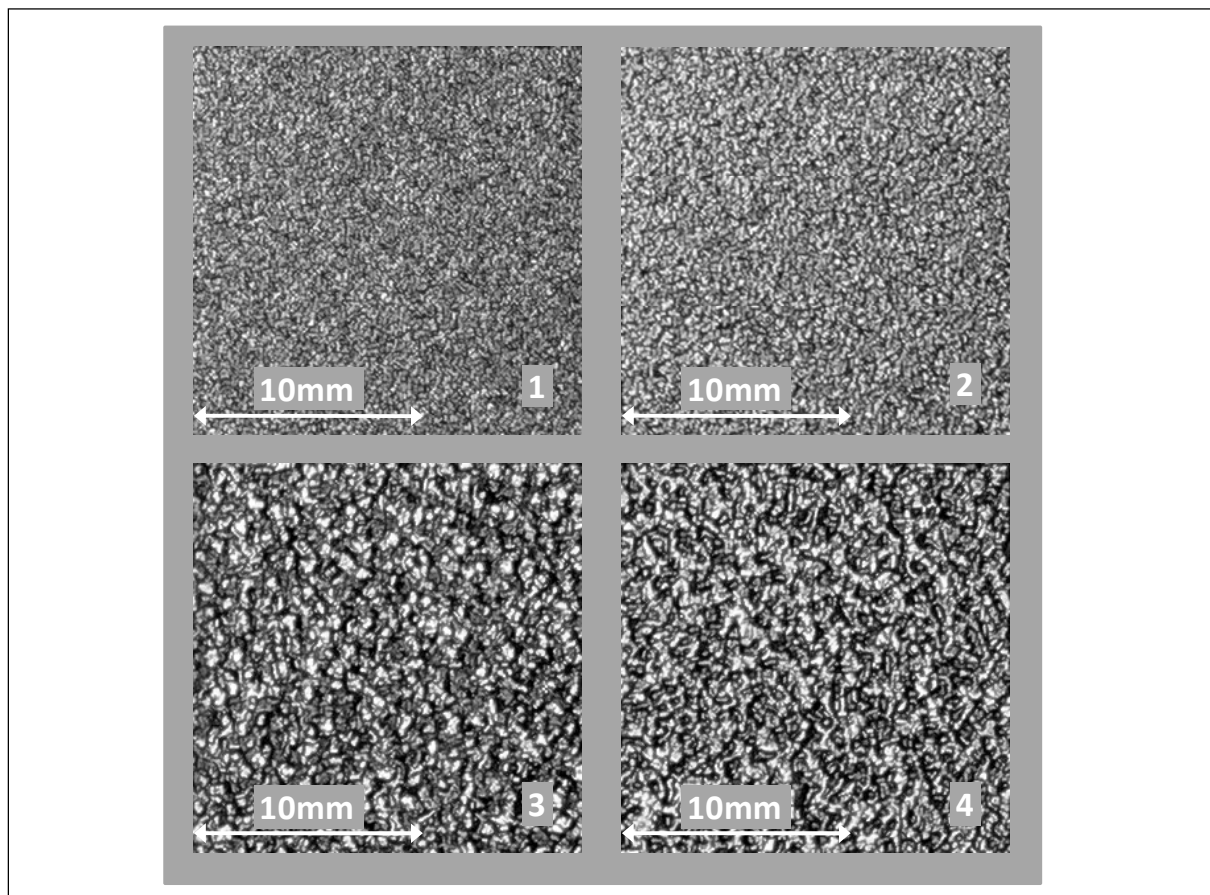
Photos der Narbungen: 1: K36, erodiertes Werkzeug; 2: K36, geätztes Werkzeug ; 3: K48, erodiertes Werkzeug ; 4: K48, geätztes Werkzeug
